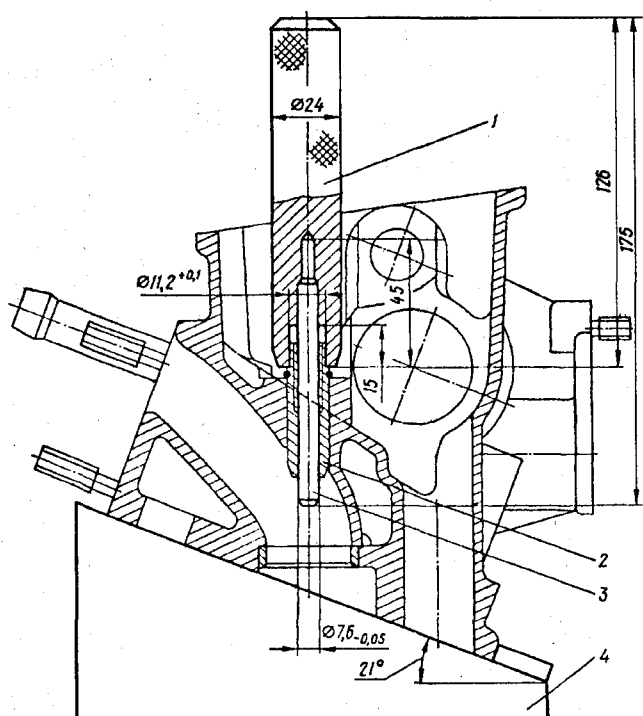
Оправка для запрессовки направляющих втулок клапанов: 1 – оправка; 2 – направляющая втулка клапана; 3 – штифт направляющий; 4 – подставка
